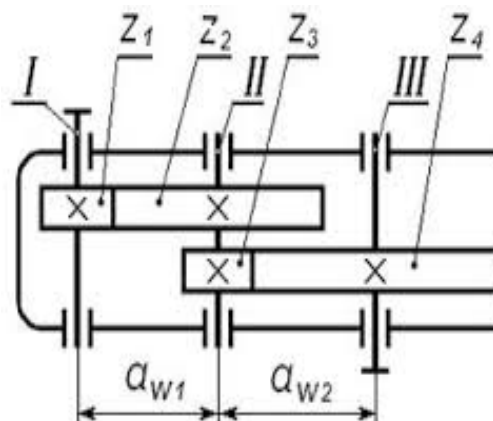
Кінематична схема двоступеневого редуктора:
